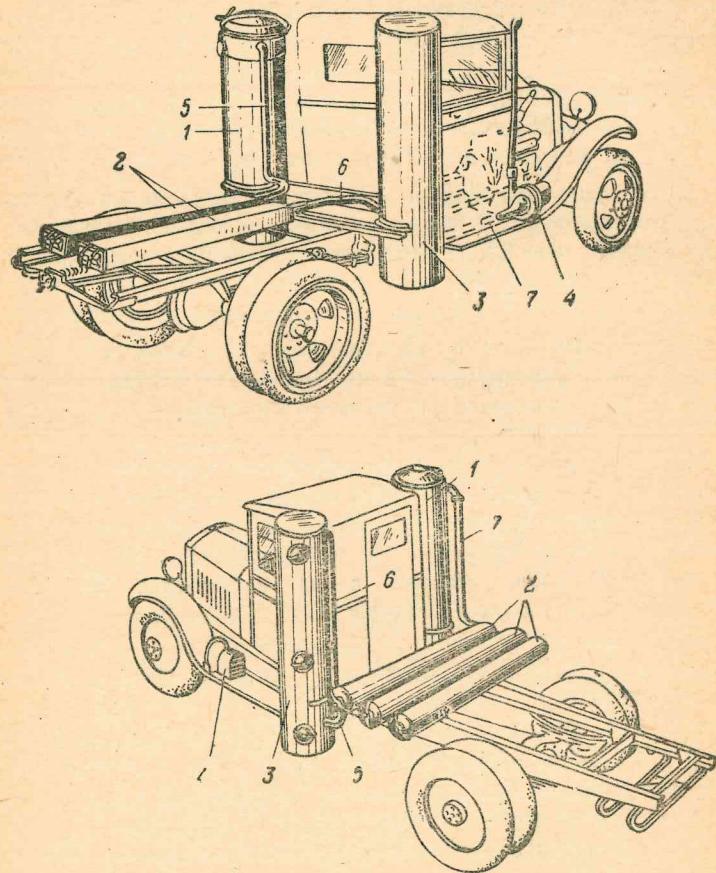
Общий вид газогенераторных автомобилей ГАЗ-42 (вверху) и ЗИС-21 (внизу) со снятыми кузовами:
